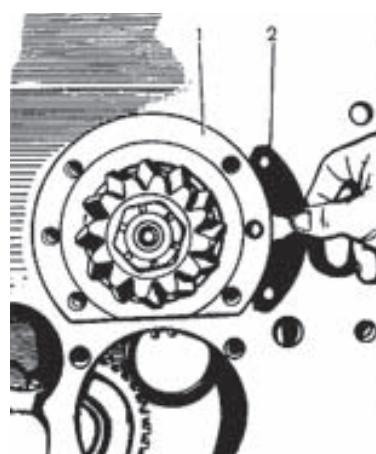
Регулировка осевого зазора в подшипниках вторичного вала: 1 — стакан подшипника вторичного вала; 2 — регулировочные прокладки
